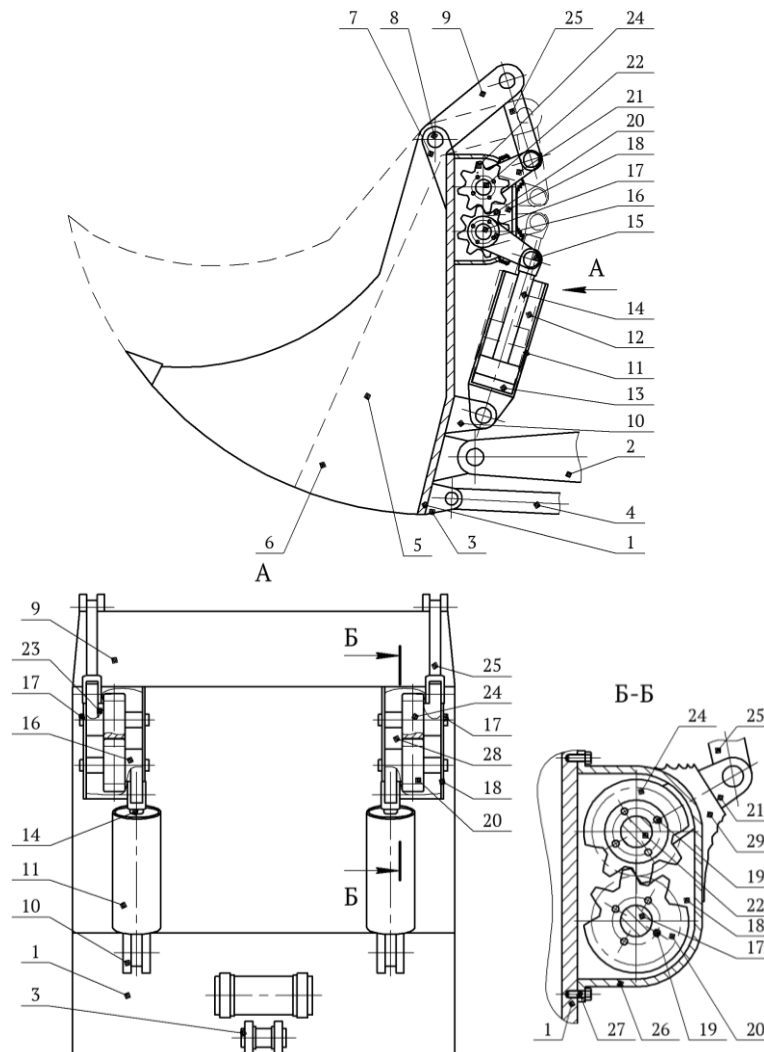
Конструкция предлагаемого гидромеханизма поворота козырька
